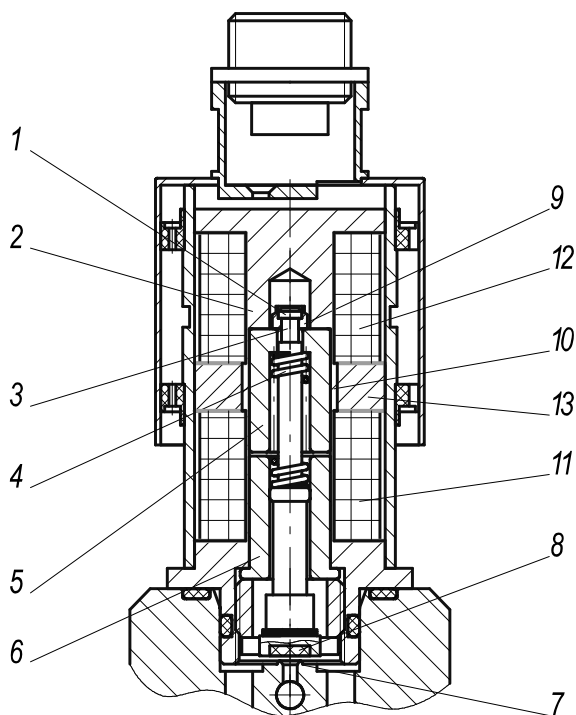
Конструктивна схема клапана з двопозиційним електромагнітним приводом: 1 — головка штока; 2 — верхній стоп; 3 — шийка штока; 4 — буферна пружина; 5 — повзун (якір); 6 — нижній стоп; 7 — сідло; 8 — золотник з гумовим ущільненням; 9 — стопорна шайба; 10 — розподільна трубка; 11 — обмотка закриття; 12 — обмотка відкриття; 13 — постійний магніт
